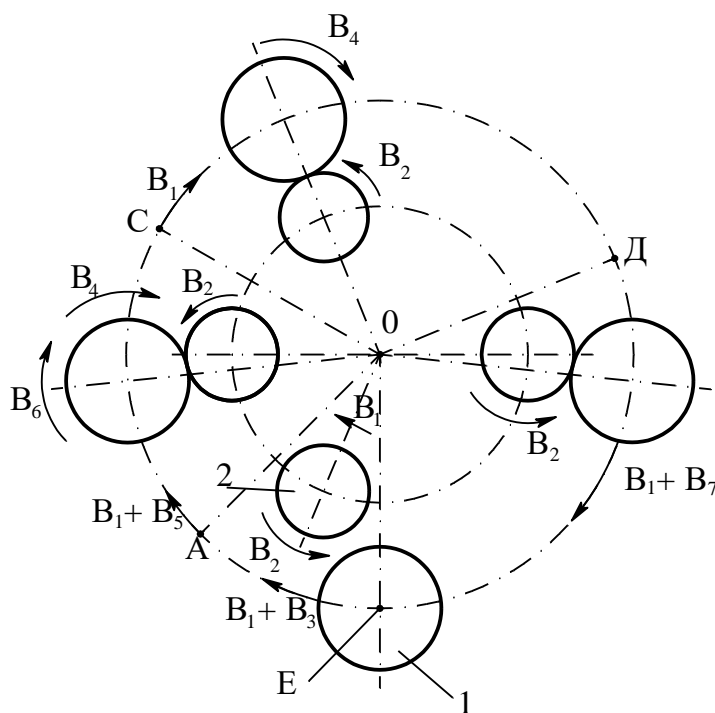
Схема зубодолбления при непрерывном транспортировании пары долбяк – заготовка
